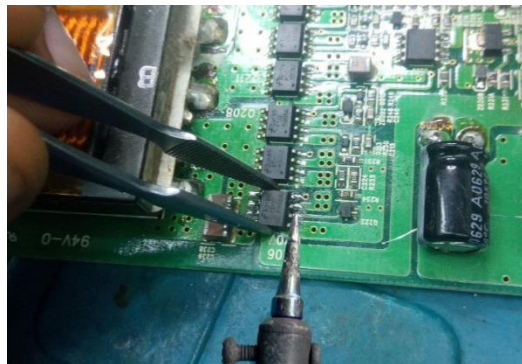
Soldado de uno de los pines del Integrado de montaje superficial – Autoría propia
